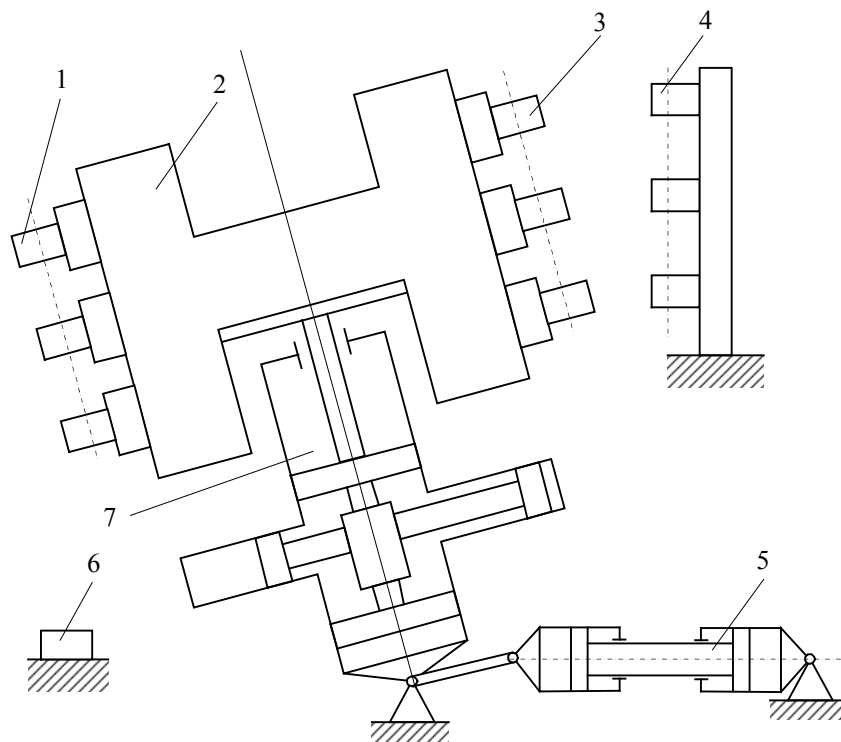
Макет автооператора металлорежущего станка мод. ГС 3 - 12:
